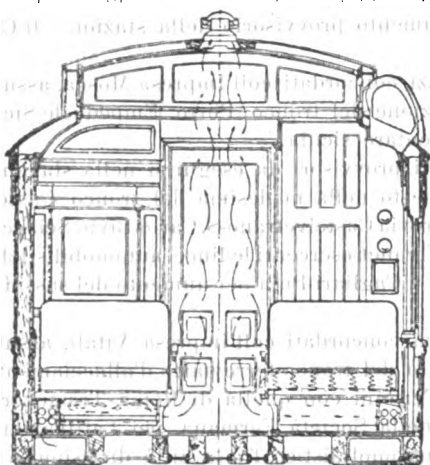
Sistema di ventilazione della Pennsylvania R.R. - Sezione trasversale.
